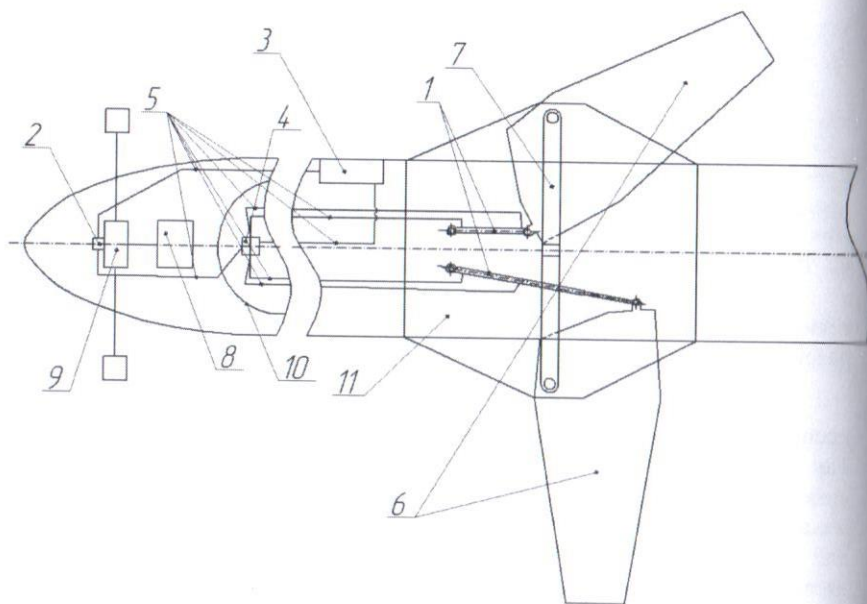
Кинематическая схема всего механизма и гидросистемы: 1- гидроцилиндр; 2-масляный насос; 3-гидробак; 4-распределитель; 5-рукав высокого давления (РВД); 6-полукрыло; 7-силовой каркас; 8-двигатель внутреннего сгорания (ДВС); 9-центральный редуктор; 10-кабина пилотов; 11-центроплан.
